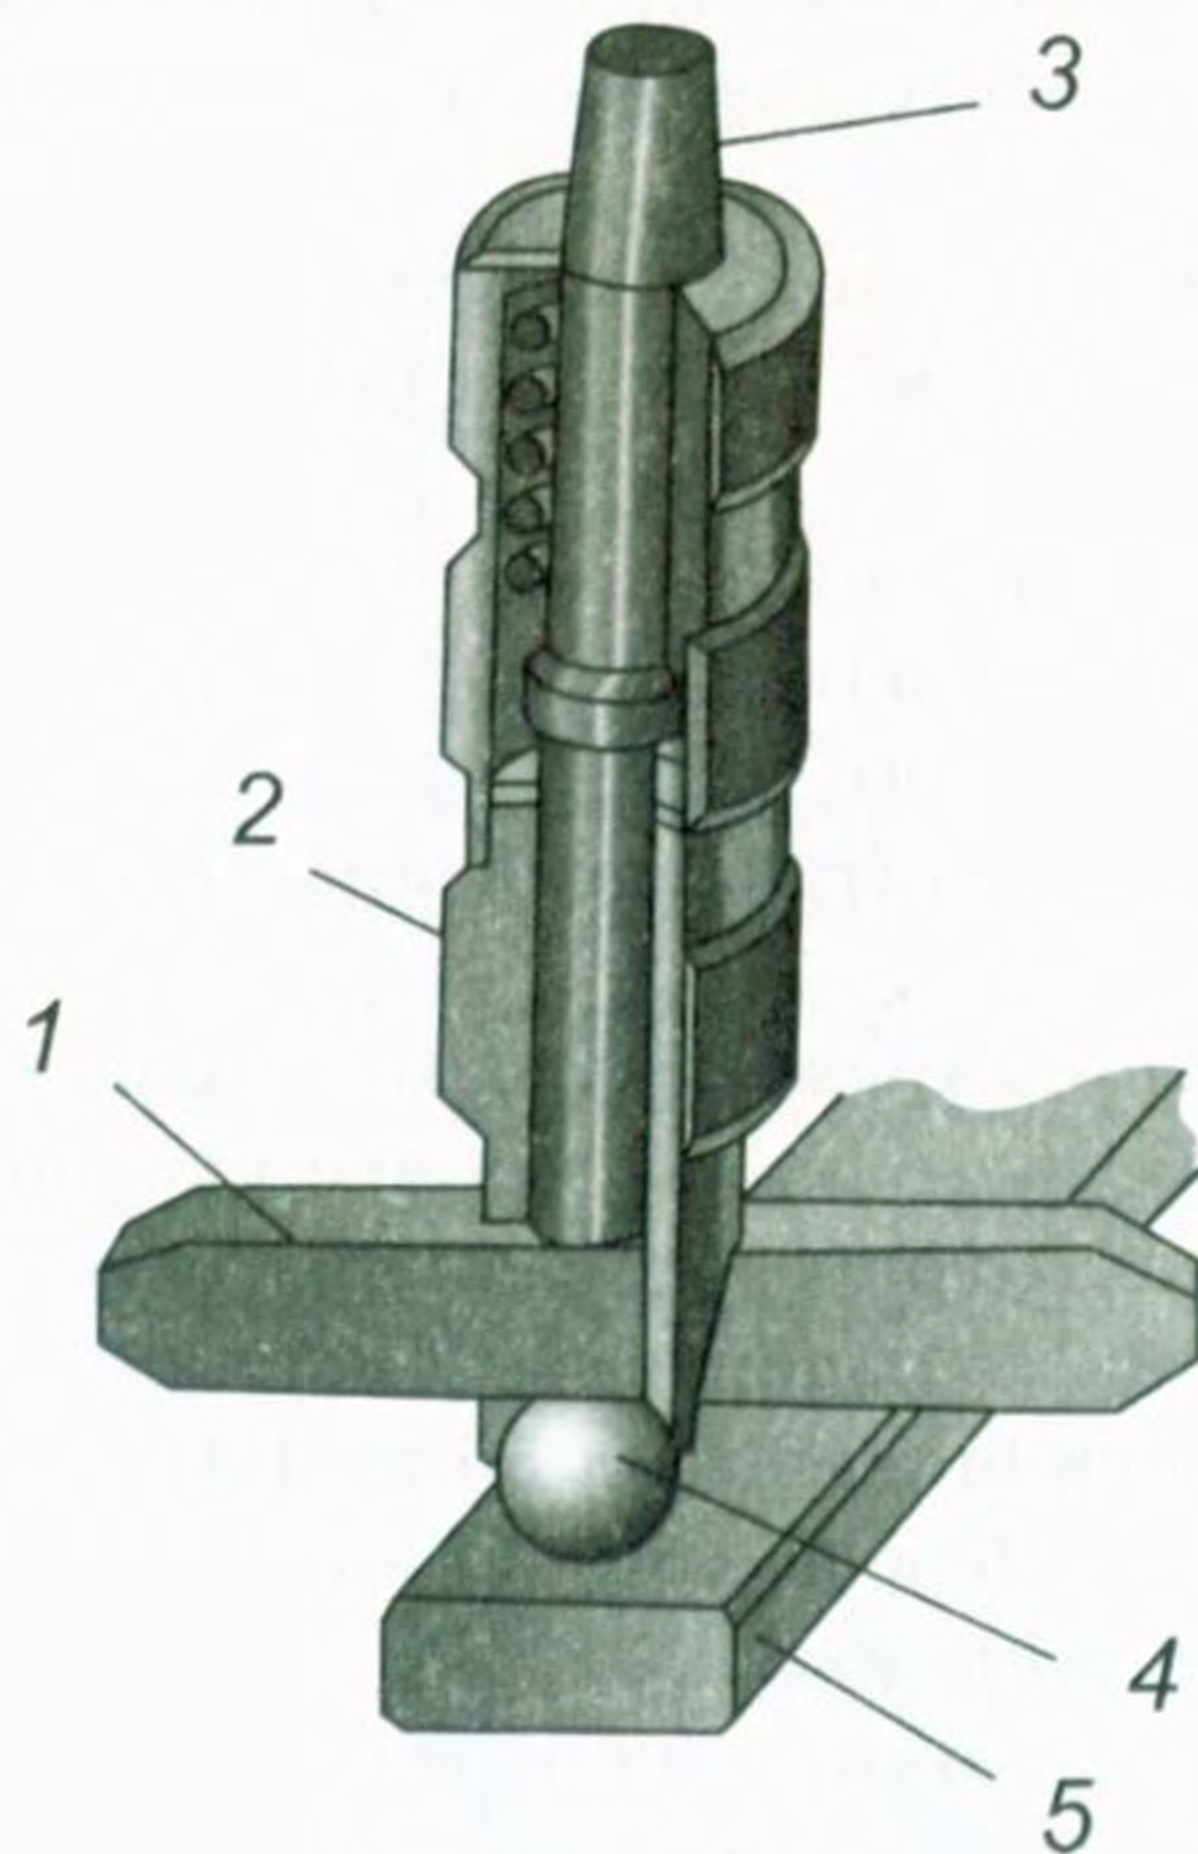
Пристрій для визначення твердості сталі до і після термічної обробки у шкільних майстернях: 1 – еталон; 2 – корпус; 3 – бойок; 4 – кулька; 5 – випробувальний зразок
